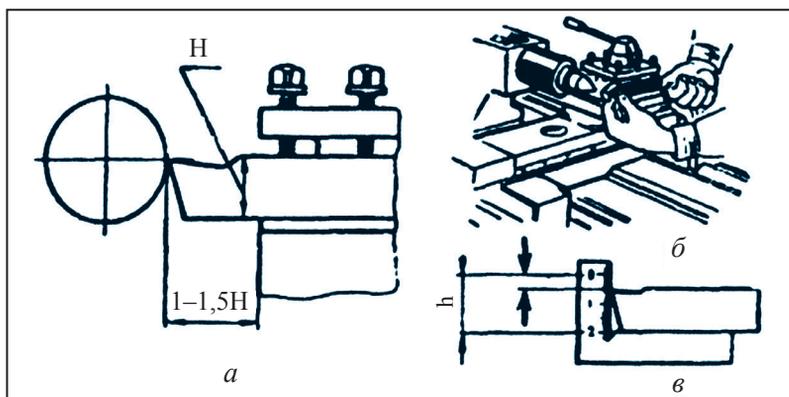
Установка резца: а – резец и его размещение; б – проверка высоты резца; в – угольный шаблон.
